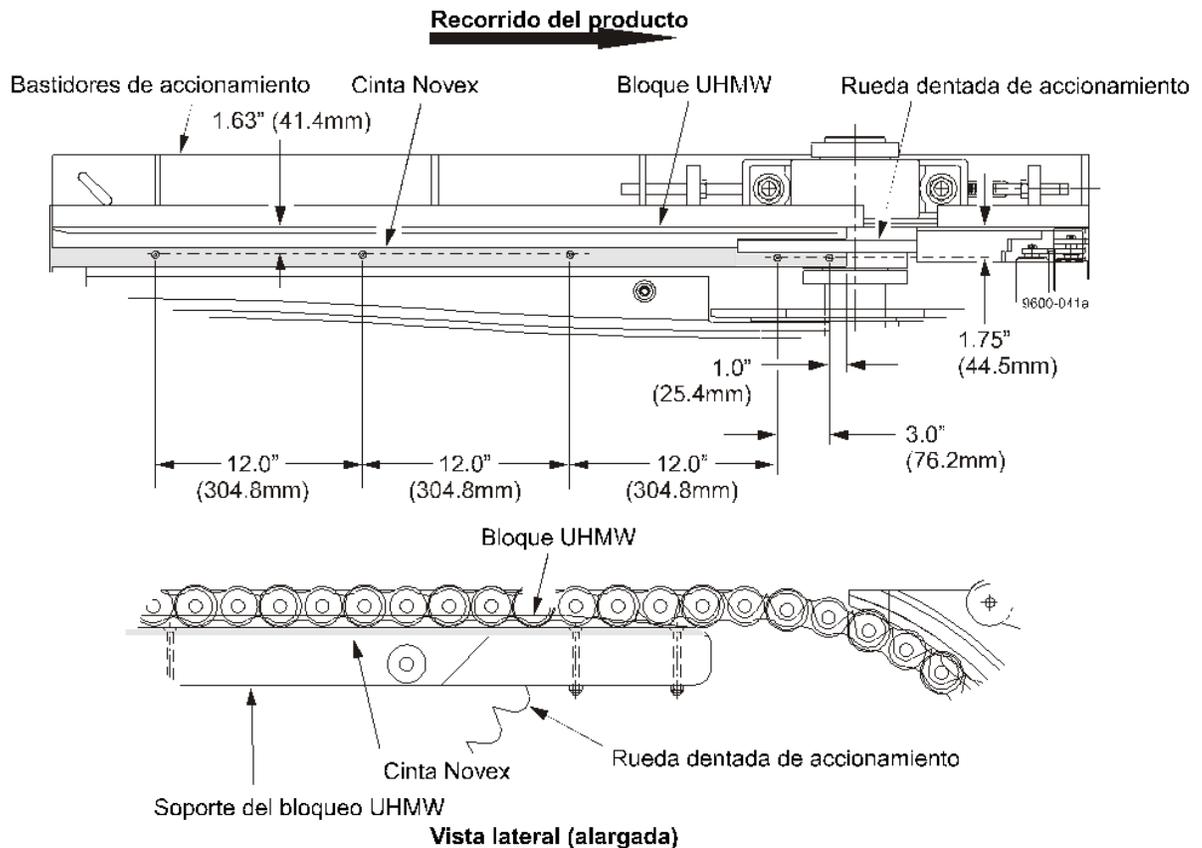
Instalación de la cinta Novex en la sección de accionamiento
